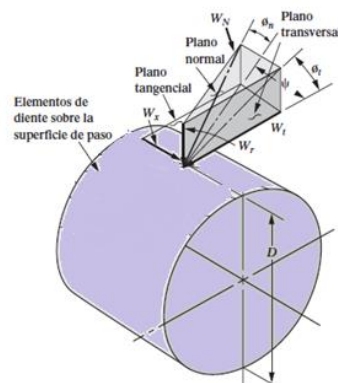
Fuerzas que actúan en la superficie de paso en el engranaje.
